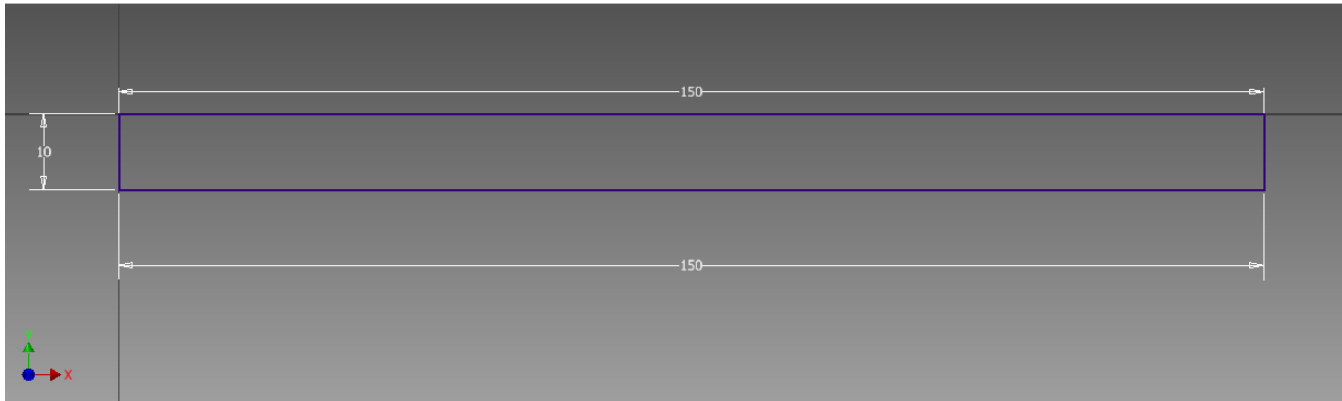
Dimensiones de una probeta para un ensayo de doblado
